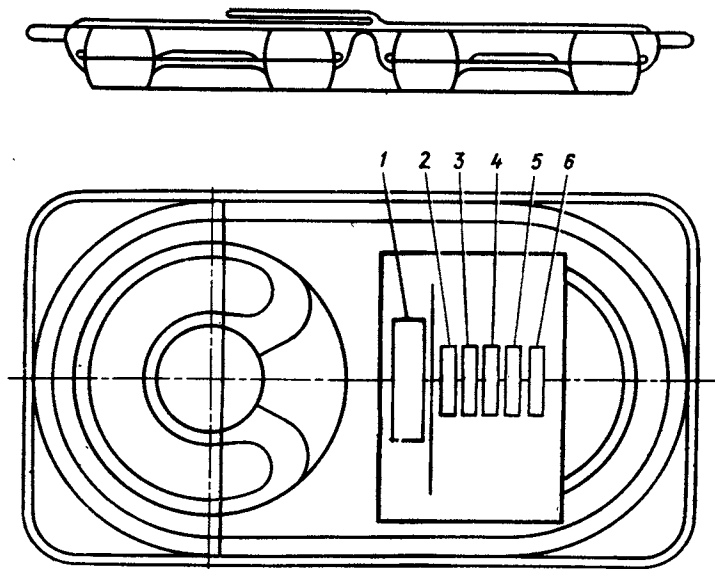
Схема упаковки и маркировки пакетов 4-3-11.010:
